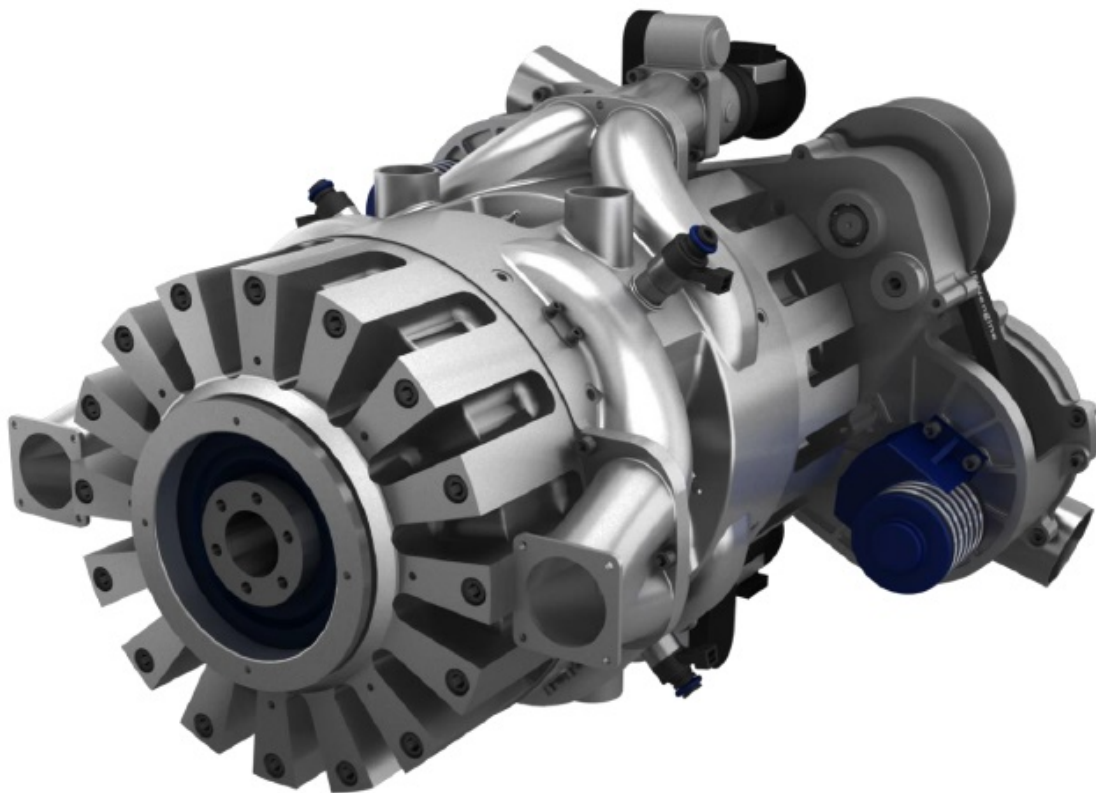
Diseño por ordenador del motor 3S ICE de InnEngine
